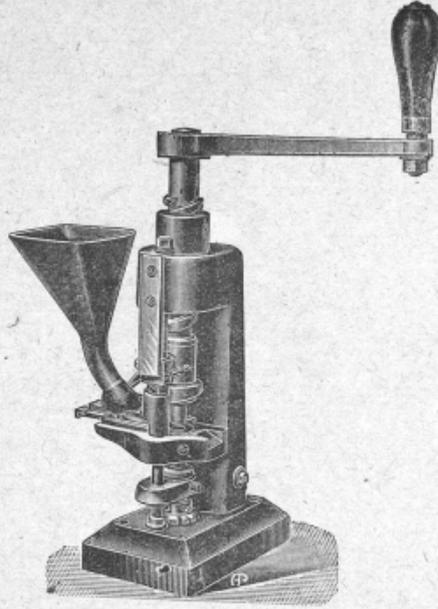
Machine à comprimer à main. Savy et Jeanjean.
